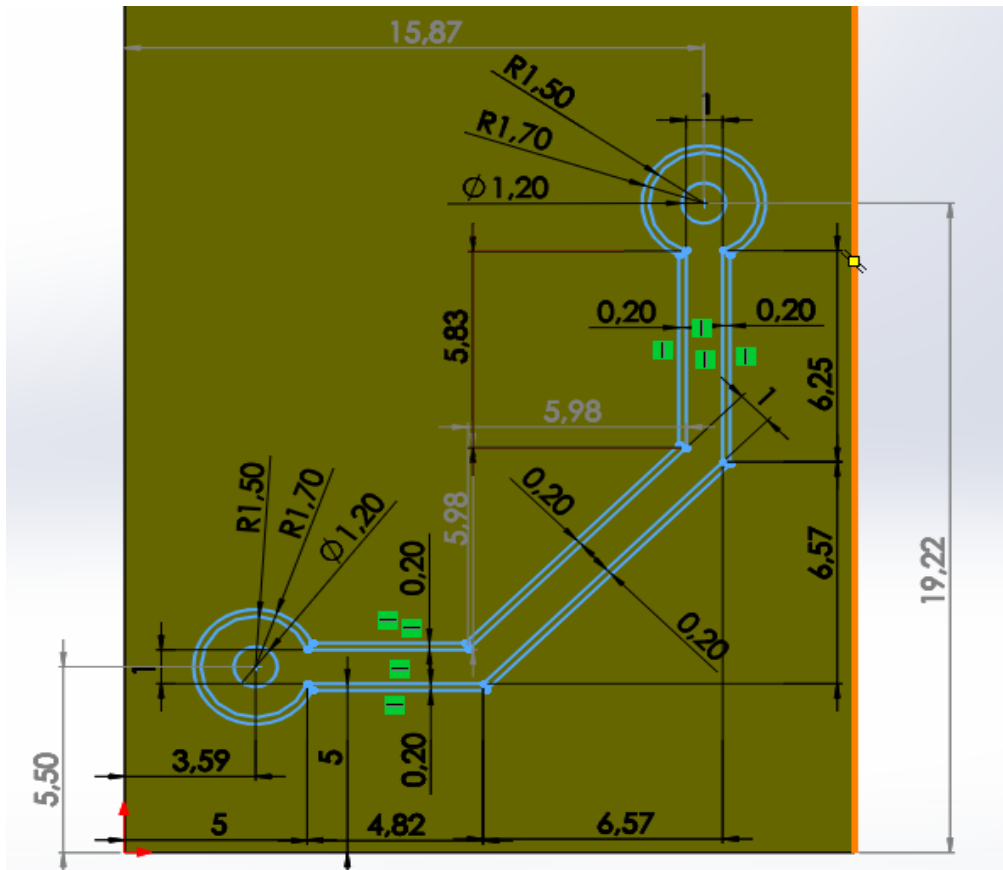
Dessin de définition d'une pad des circuits électriques.
